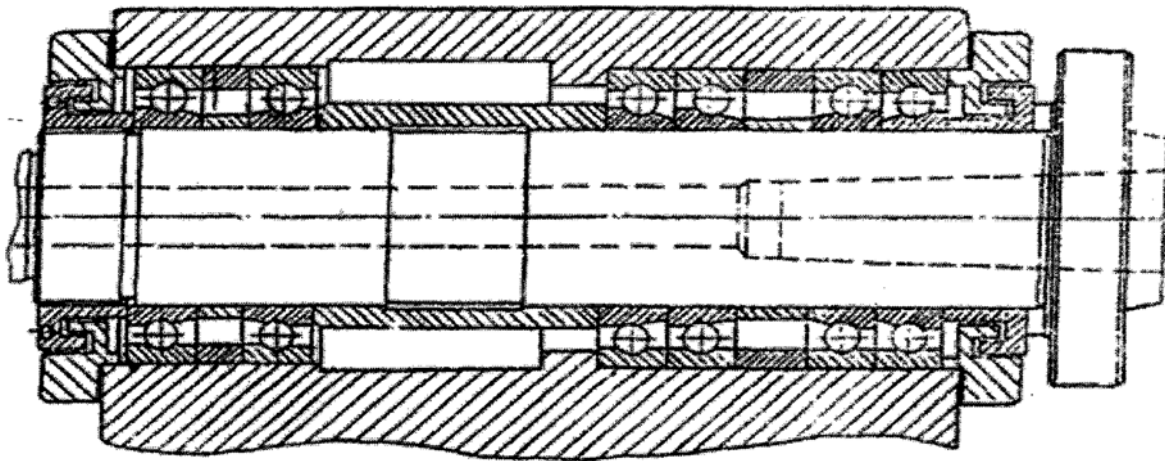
Шпиндельный узел станка с ЧПУ на роликоподшипниках типа 3182100 в обеих опорах и на упорно-радиальном подшипнике типа 178000 в передней опоре
